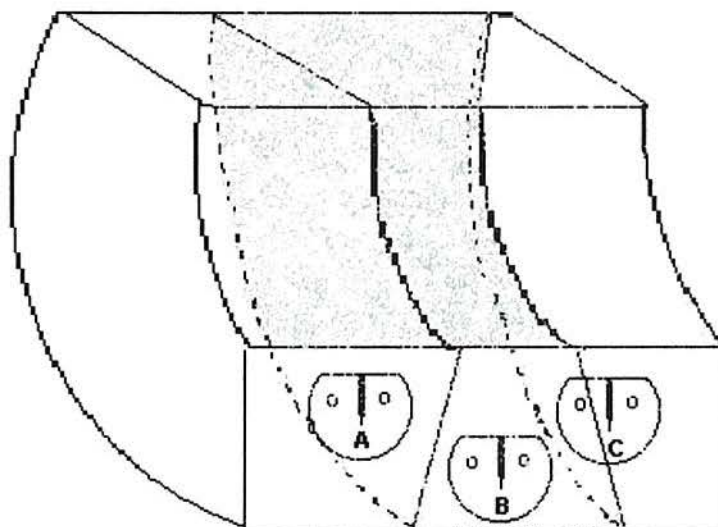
Localização dos corpos de prova na junta soldada: a) zona afetada pelo calor; b) metal de solda; c) zona de ligação
